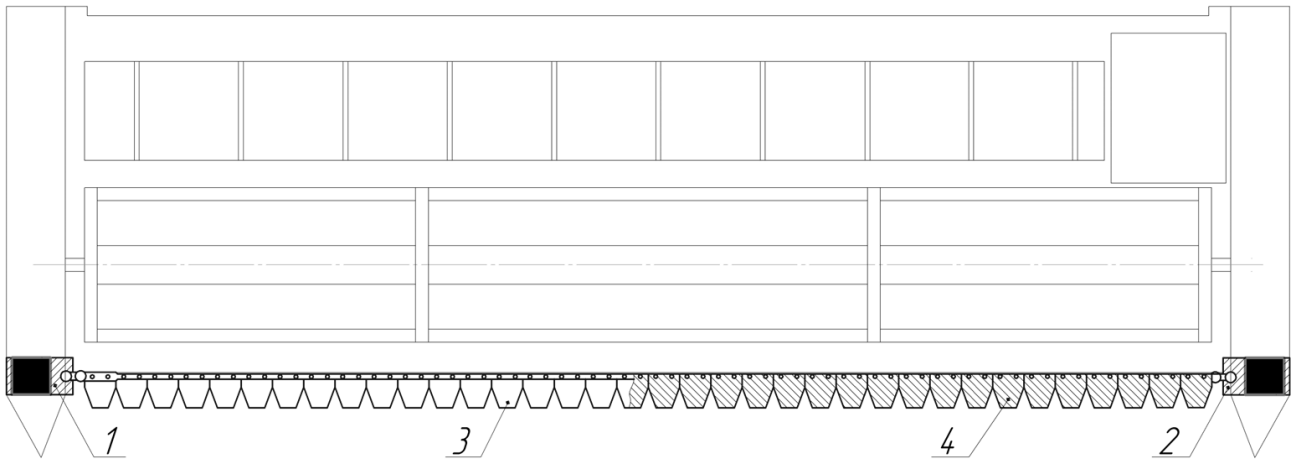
Жатка з фронтальним розташуванням приводних ДПЛАД: 1 – ДПЛАД, який приводить у дію верхню ножову смугу; 2 – ДПЛАД, що забезпечує рух нижньої ножової смуги; 3 – верхня ножова смуга ріжучого апарата; 4 – нижня ножова смуга ріжучого апарата [2].
